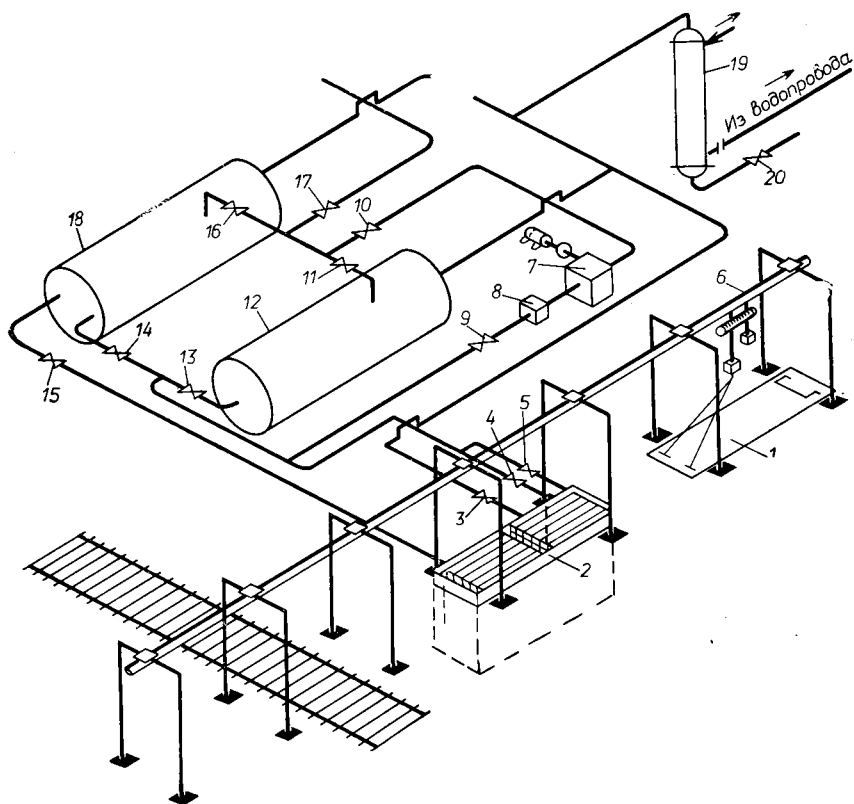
Гидрокинематическая схема шпалопропиточной установки
